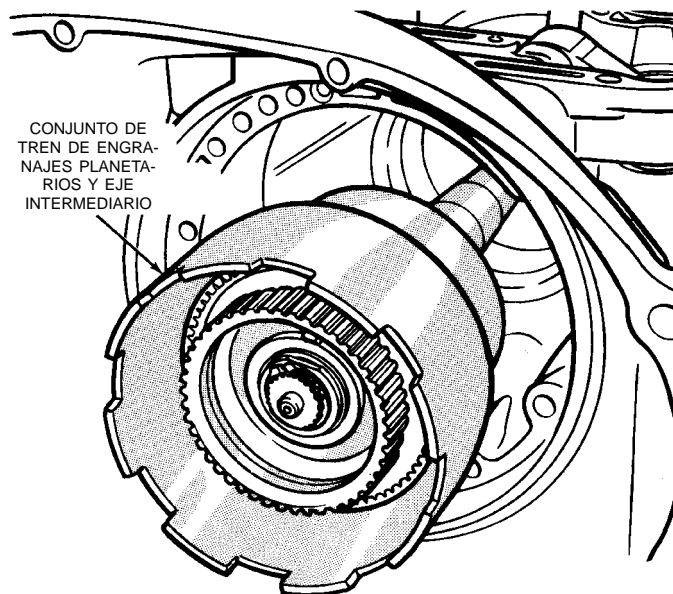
Desmontaje del conjunto del tren de engranajes planetarios y el eje intermediario
